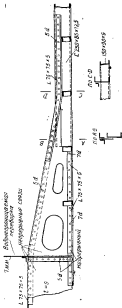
Соединение стержня лобового дни с полуцилиндрическим стержнем для лобового дни.
